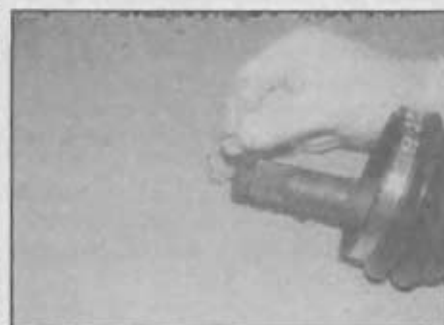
Установите новое стопорное кольцо в канавку приводного вала
